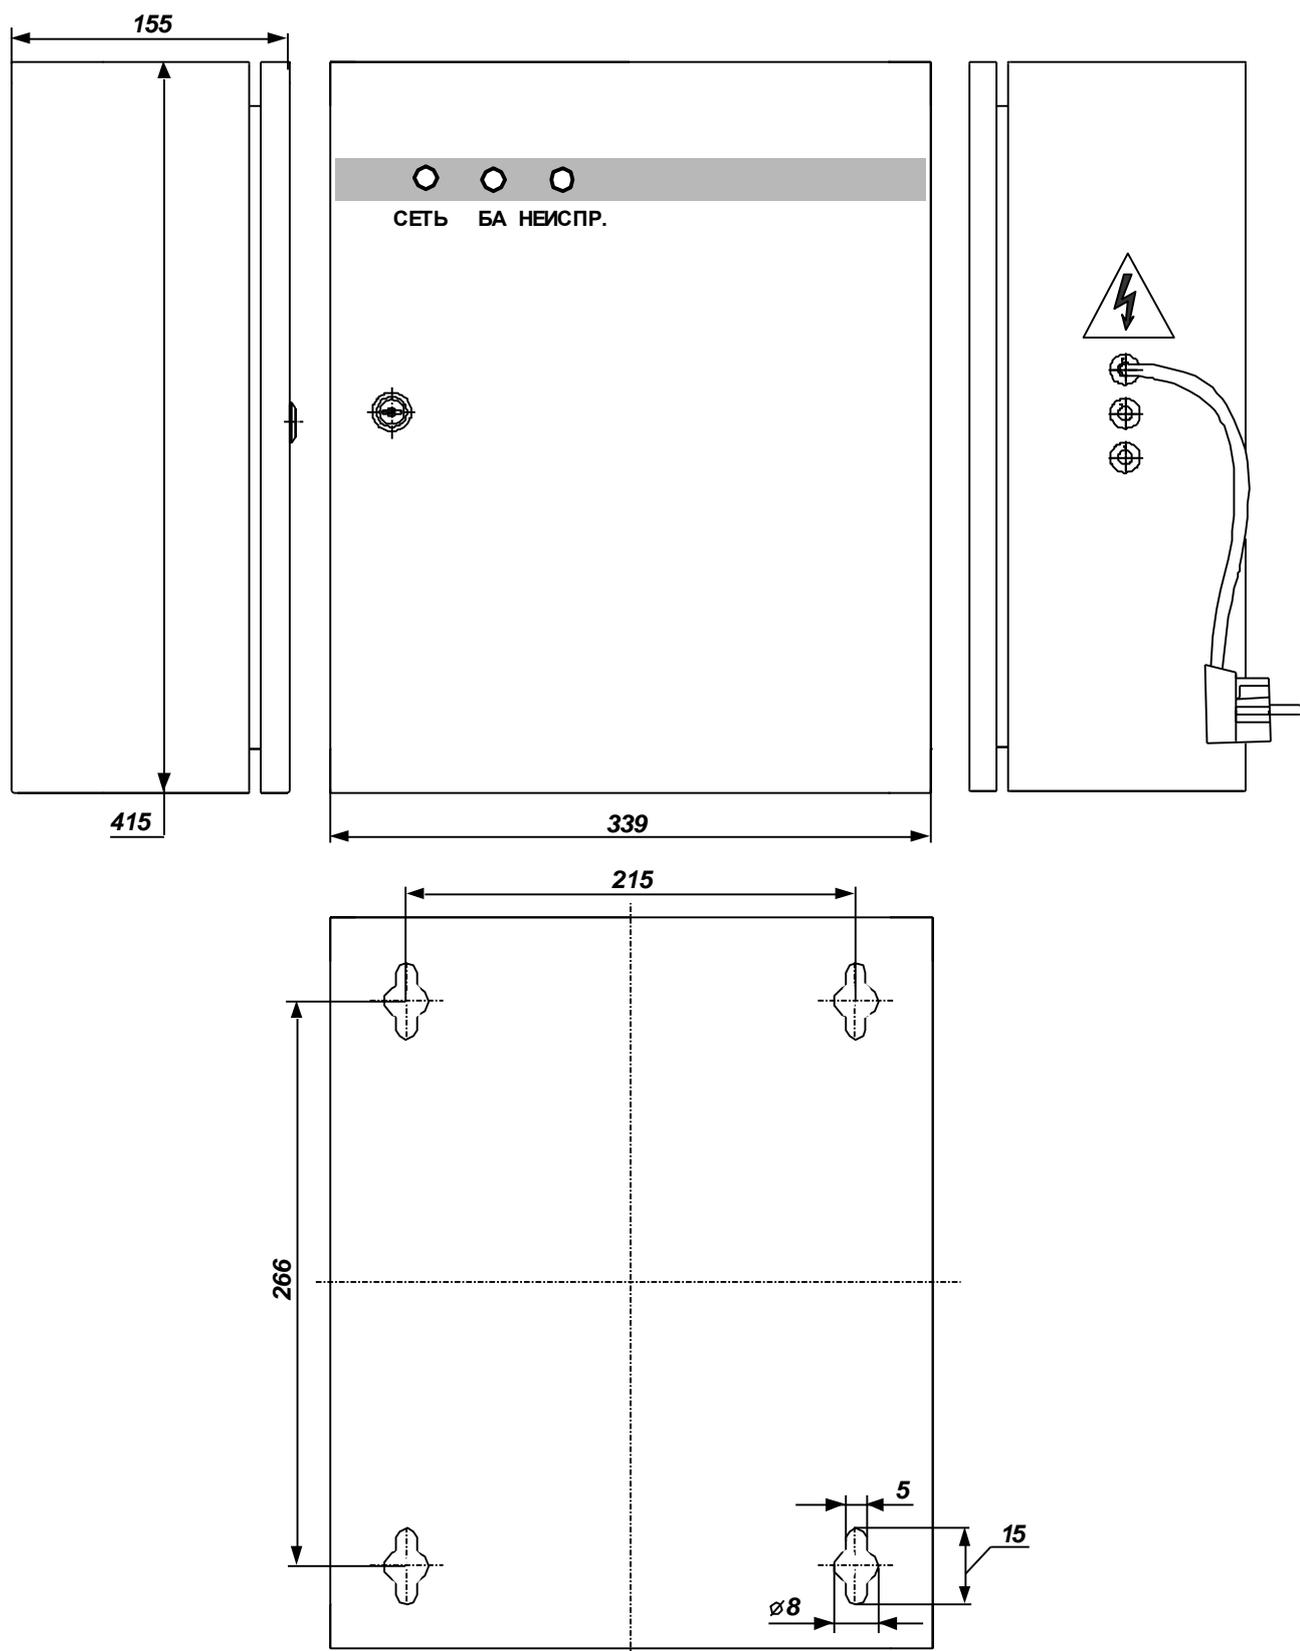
Внешний вид БЦП «Р-08» исп.8 (габаритные размеры)
